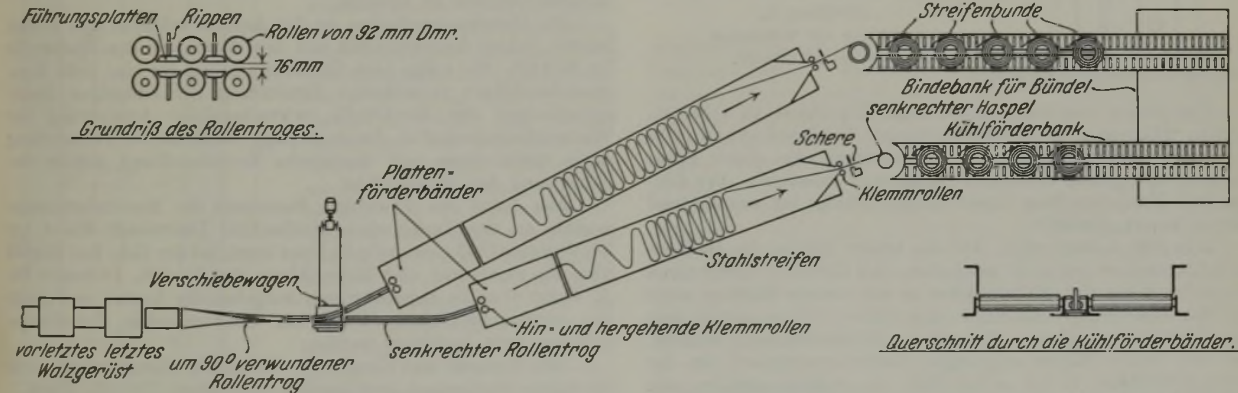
Grundriß der Streifen-Fördervorrichtungen vom Walzgerüst zur Bindebank.
